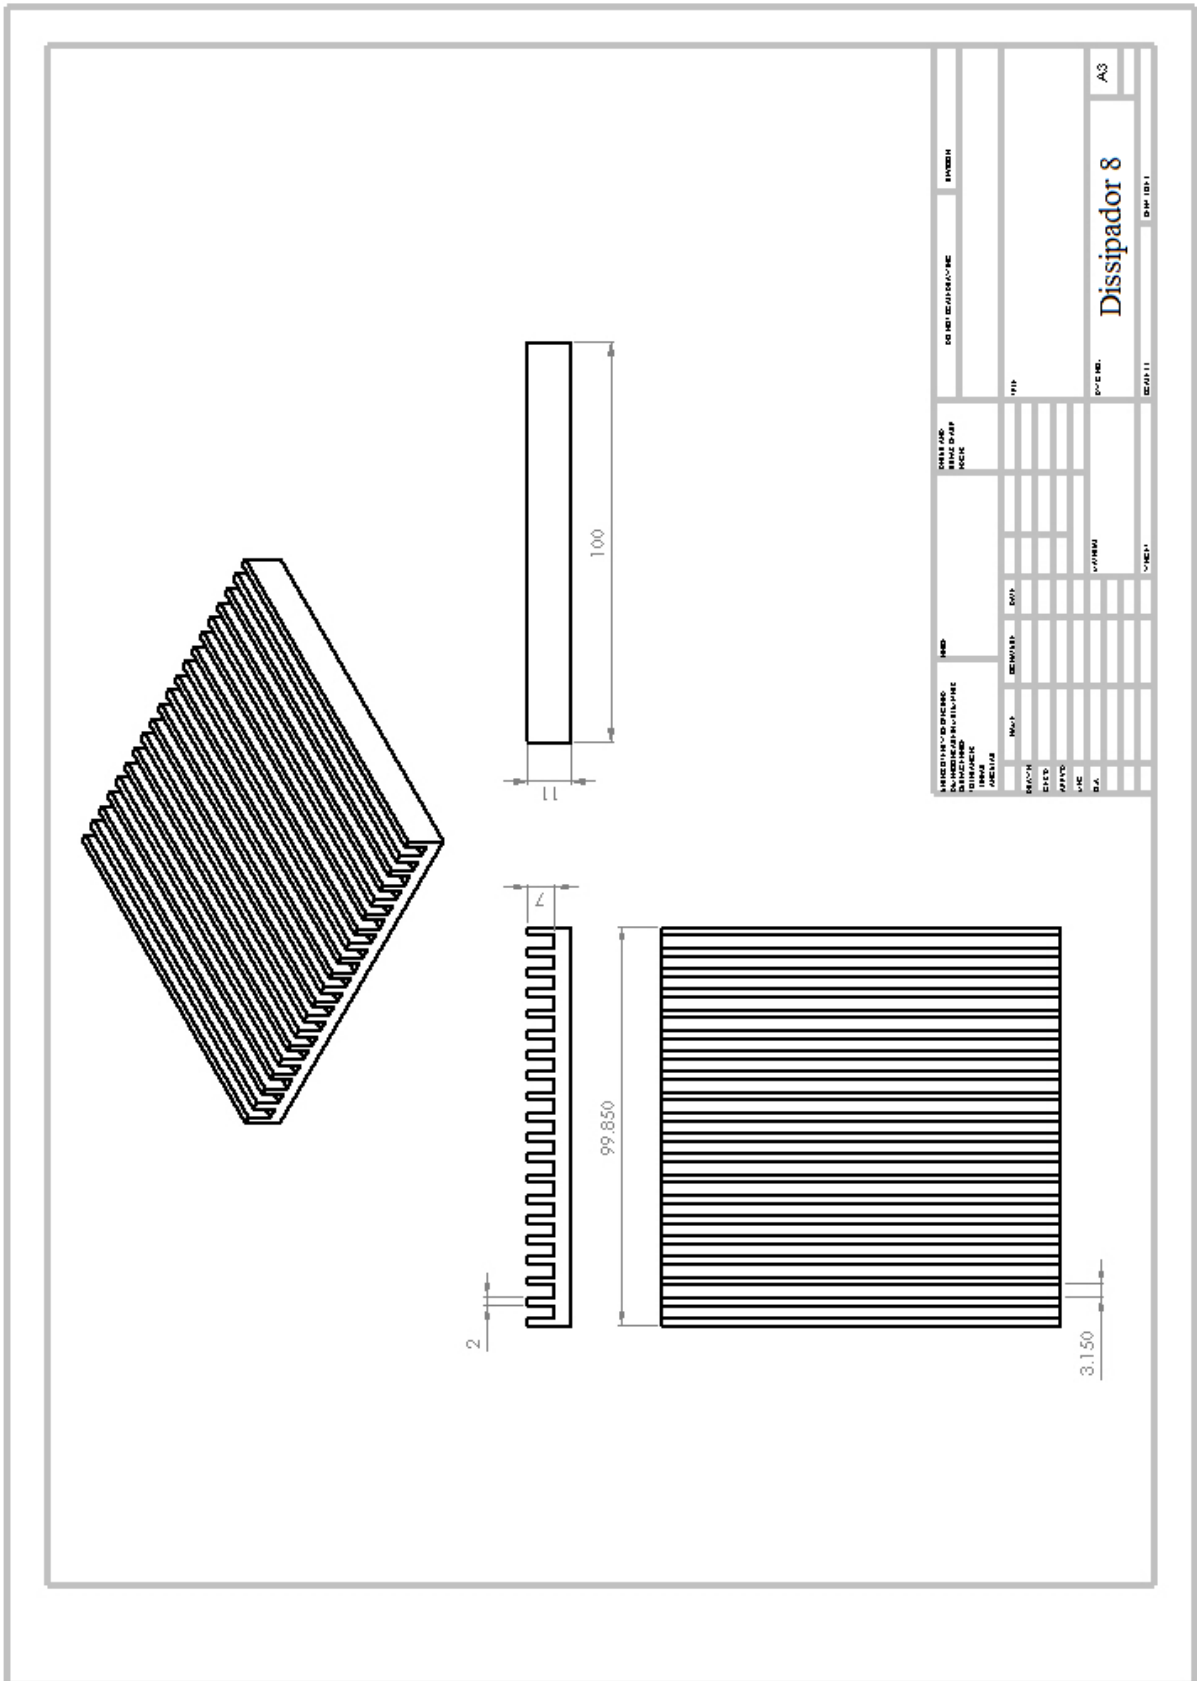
Desenho técnico utilizado para confecção do Dissipador 8.
